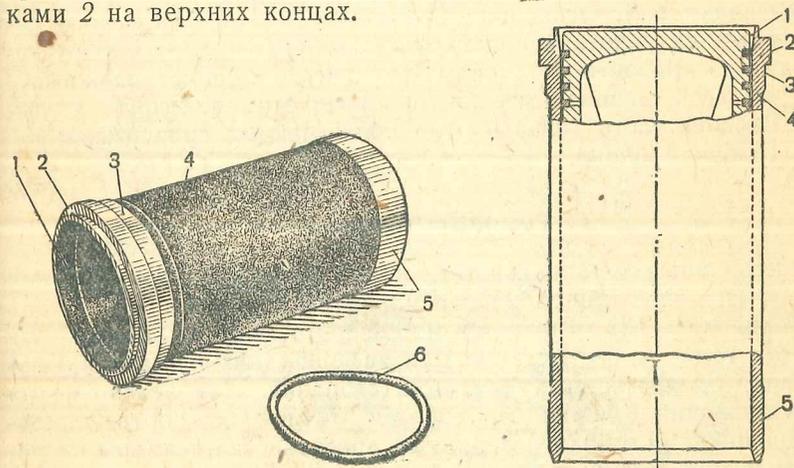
Общий вид и разрез цилиндровой гильзы.
